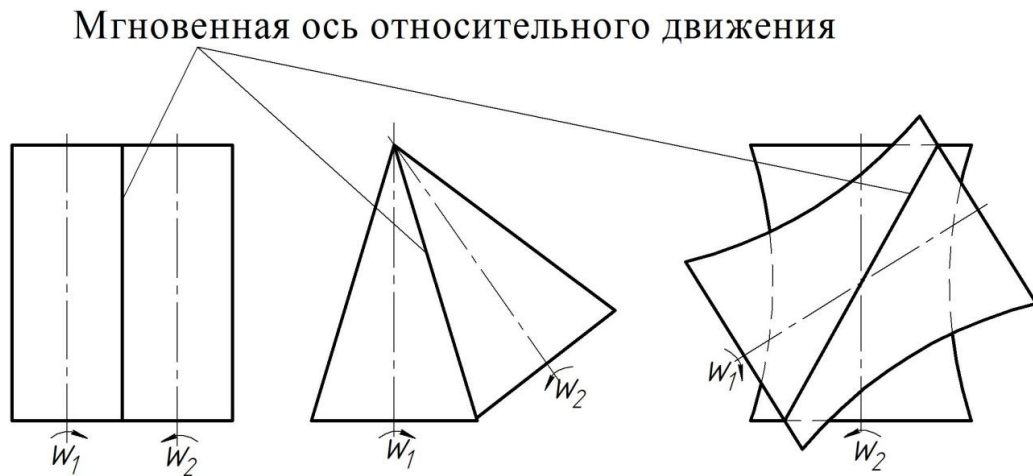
Аксоидная поверхность зубчатого колеса передачи
